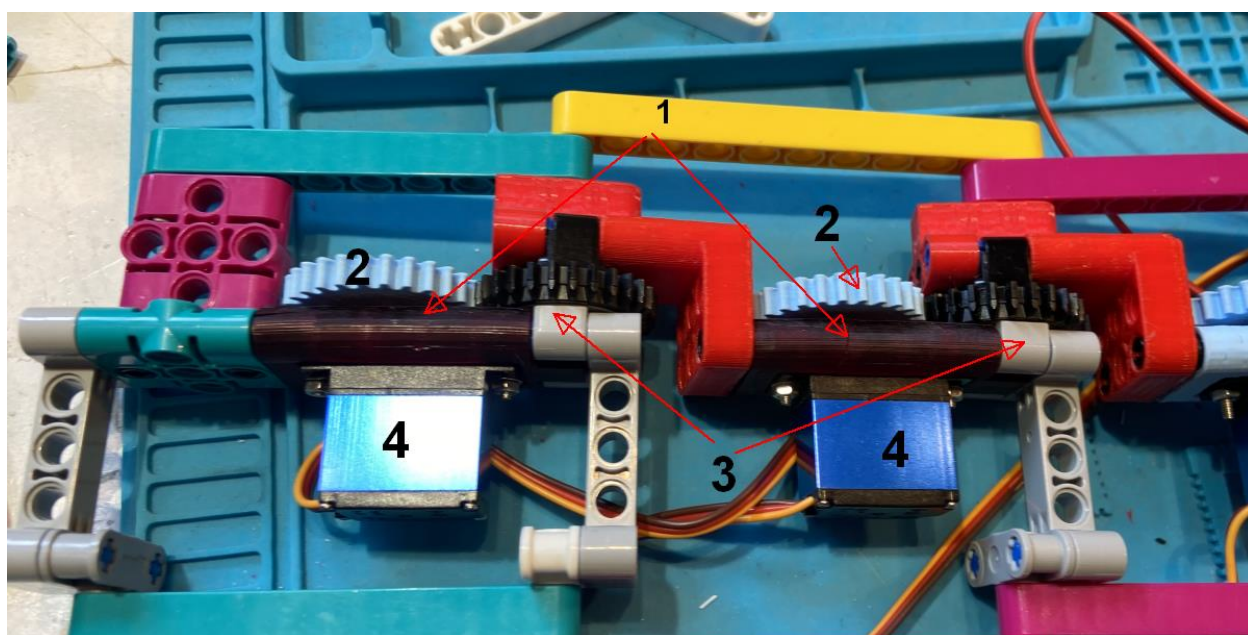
Крепление сервомашин с деталями Lego. 1- отпечатанные на фотополимерном принтере крепления сервомашин 4, 2- отпечатанные на FDM принтере шестерни, 3 – детали Lego 99009/99010.
